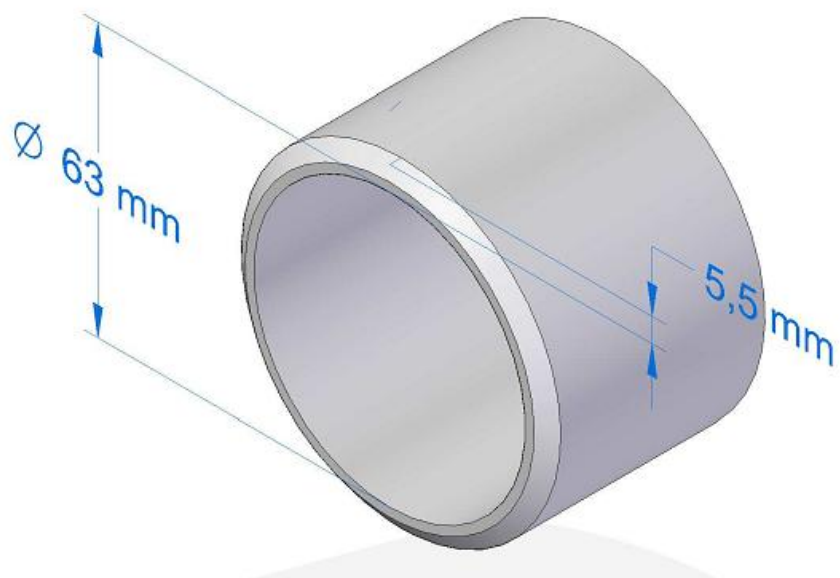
Dimensões do duto utilizado para soldagem.
